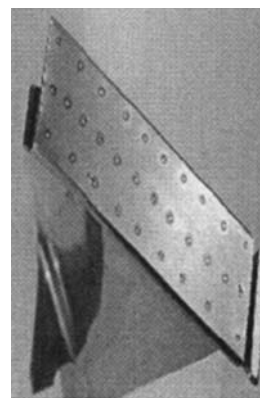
Замок лопатки, восстановленный контактной сваркой
